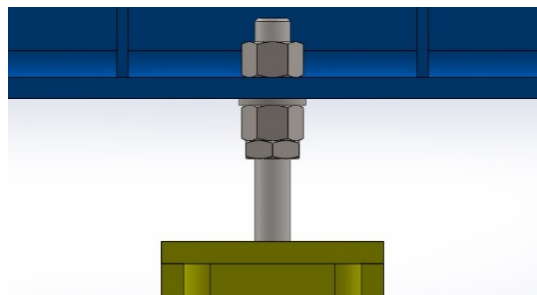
Configuración de la unión de estructura principal y bancada
